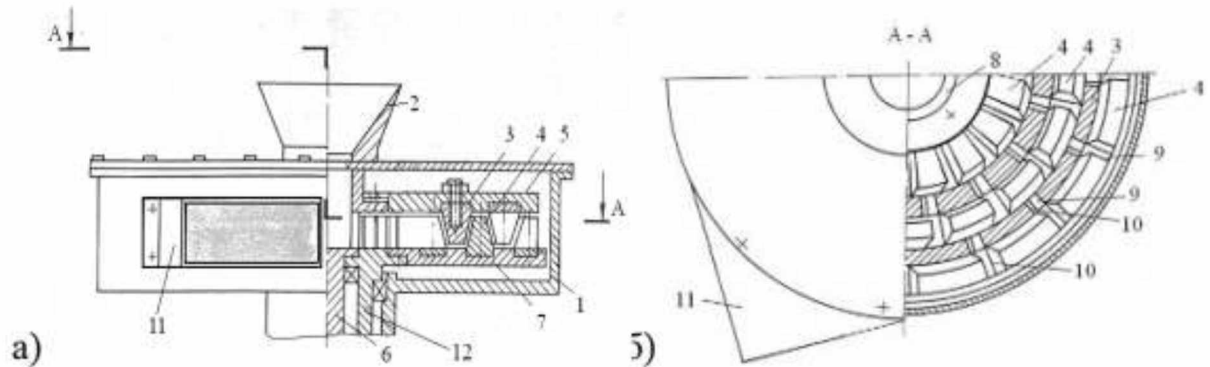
Схема відцентрово-роторного подрібнювача (а) і його ріжучих поверхонь (б): 1 - корпус; 2 - патрубок завантажувальний; 3, 4 - ріжучі елементи; 5 - диск-ротор верхній; 6 - вал внутрішній; 7 - диск-ротор нижній; 8 - вікна радіальні; 9 - канали (пази); 10 - стінка каналу; 11 - патрубок вивантажний; 12 - вал.
